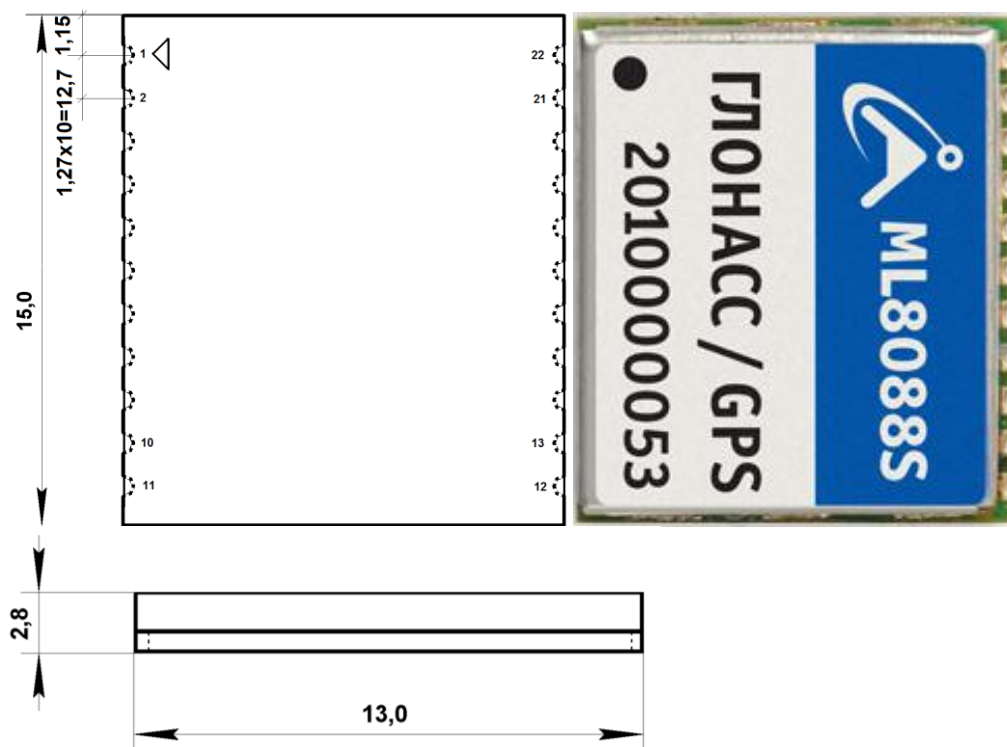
Габаритно-присоединительные размеры модуля ML8088s.
